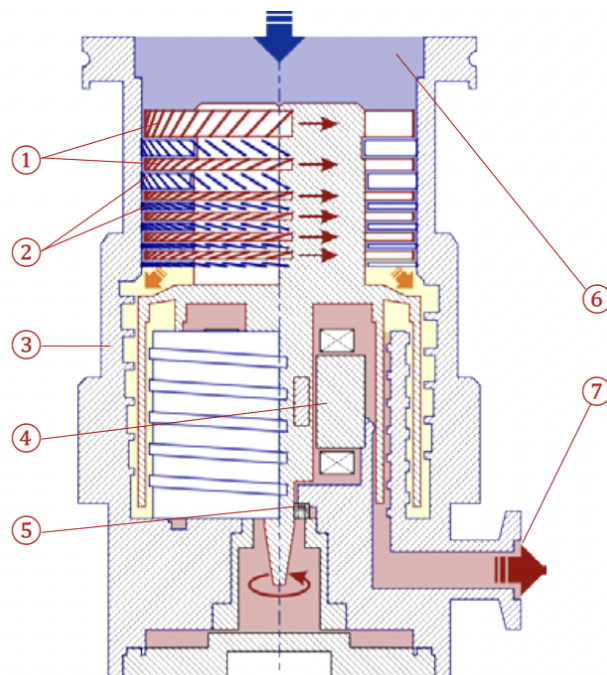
Конструкция турбомолекулярного насоса. 1 — ротор, 2 — статор, 3 — корпус насоса, 4 — электродвигатель, 5 — нижний шарикоподшипник, 6 — высоковакуумный входной фланец, 7 — выпускной форвакуумный фланец
